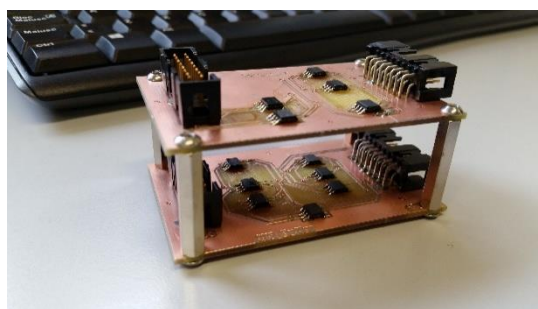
SCHEDE BUFFER AMC E BUFFER PA
